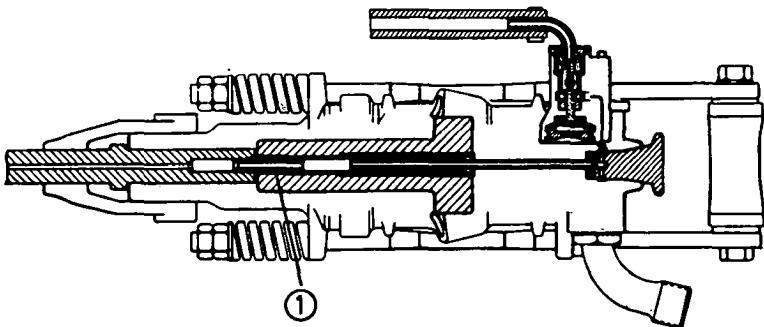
Utilisation d'un manchon de plastique pour assurer l'étanchéité de la conduite d'eau.
